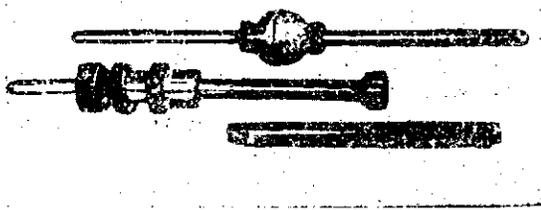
Приспособление для фрезеровки торца втулки, направляющей клапан и для развертки ее.
